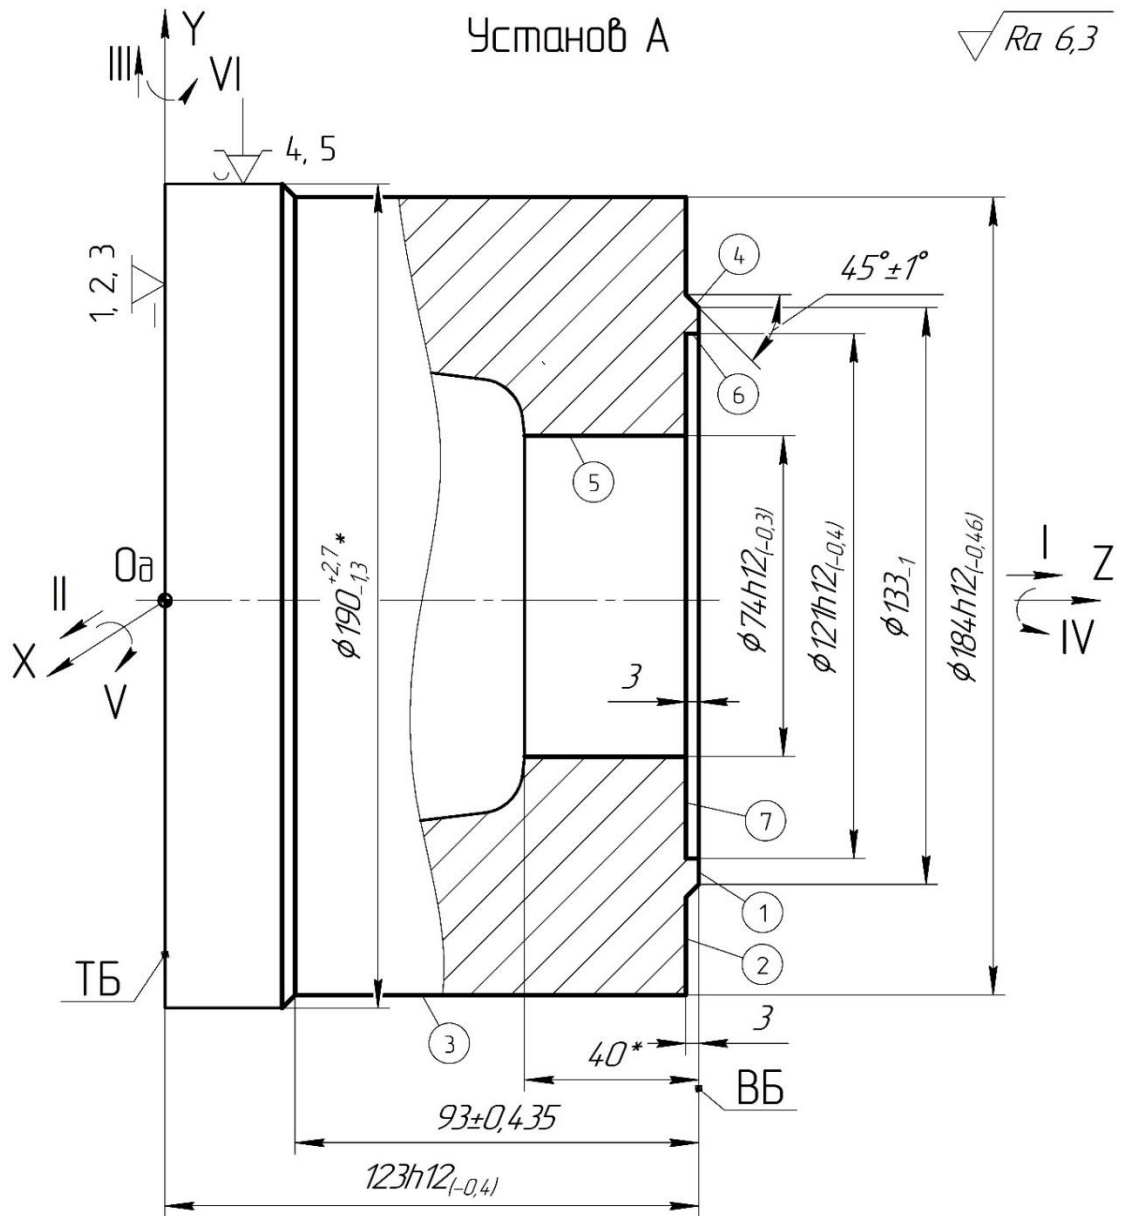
Схема установки заготовки на операції 015 «Токарна з ЧПК».
